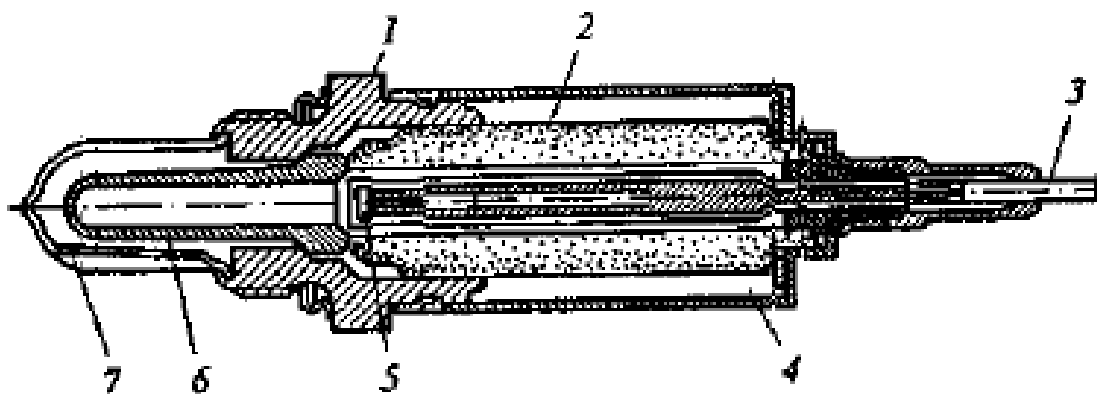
Датчик кислорода: 1 и 2 – соответственно металлический и керамический корпуса; 3 – выходной кабель; 4 – внешний кожух; 5 – контактный наконечник; 6 – активный элемент (колпачок); 7 – защитный кожух с прорезями
